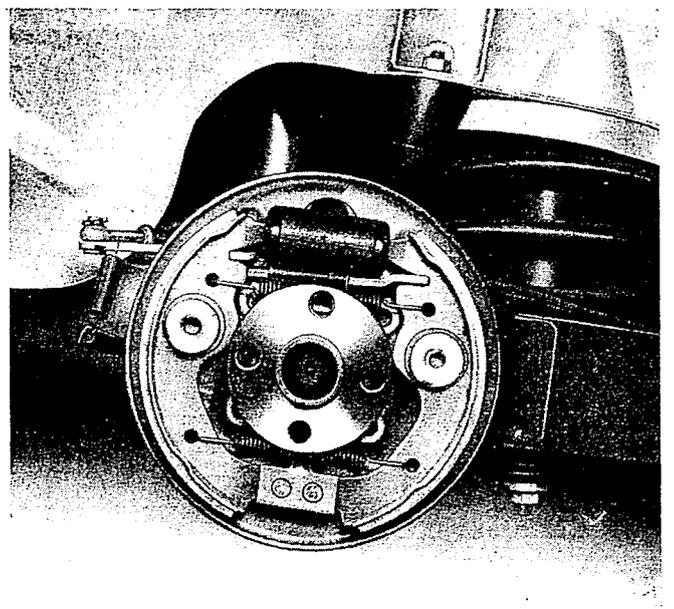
Hinterer, rechter Bremsträger ohne Trommel.
